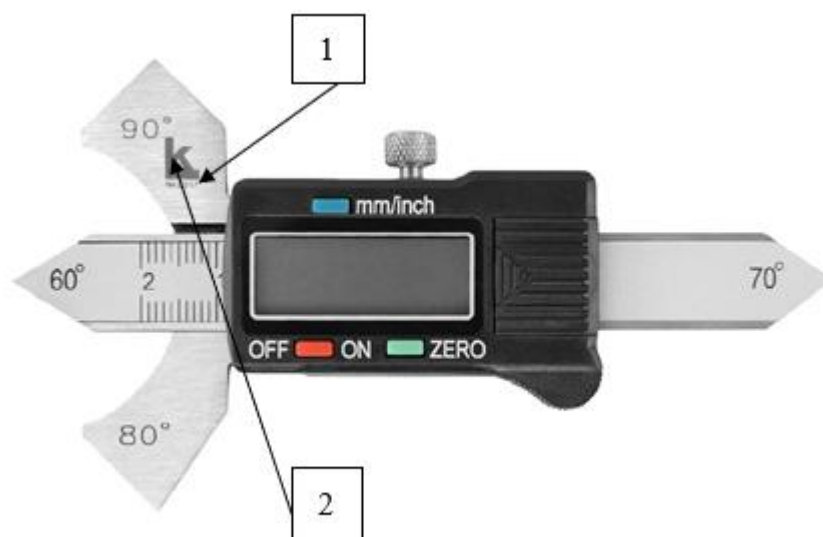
Общий вид шаблона сварщика Ушера – Маршака цифрового
